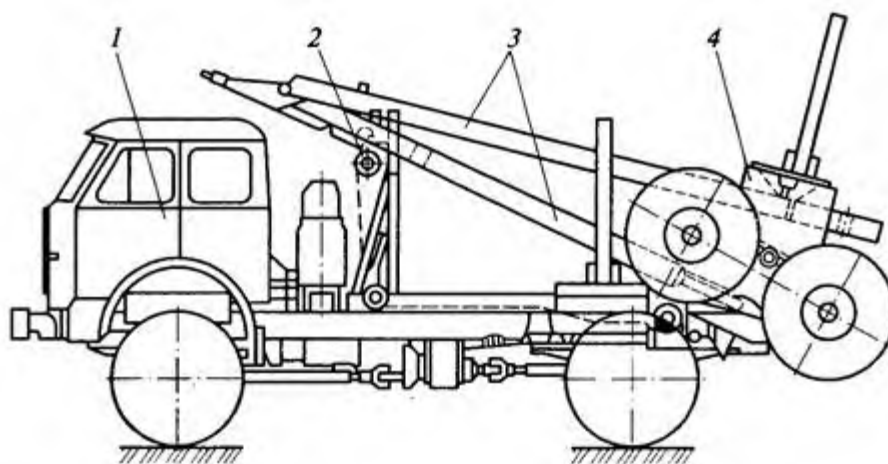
Общий вид автомобиля со складывающим дышлом
